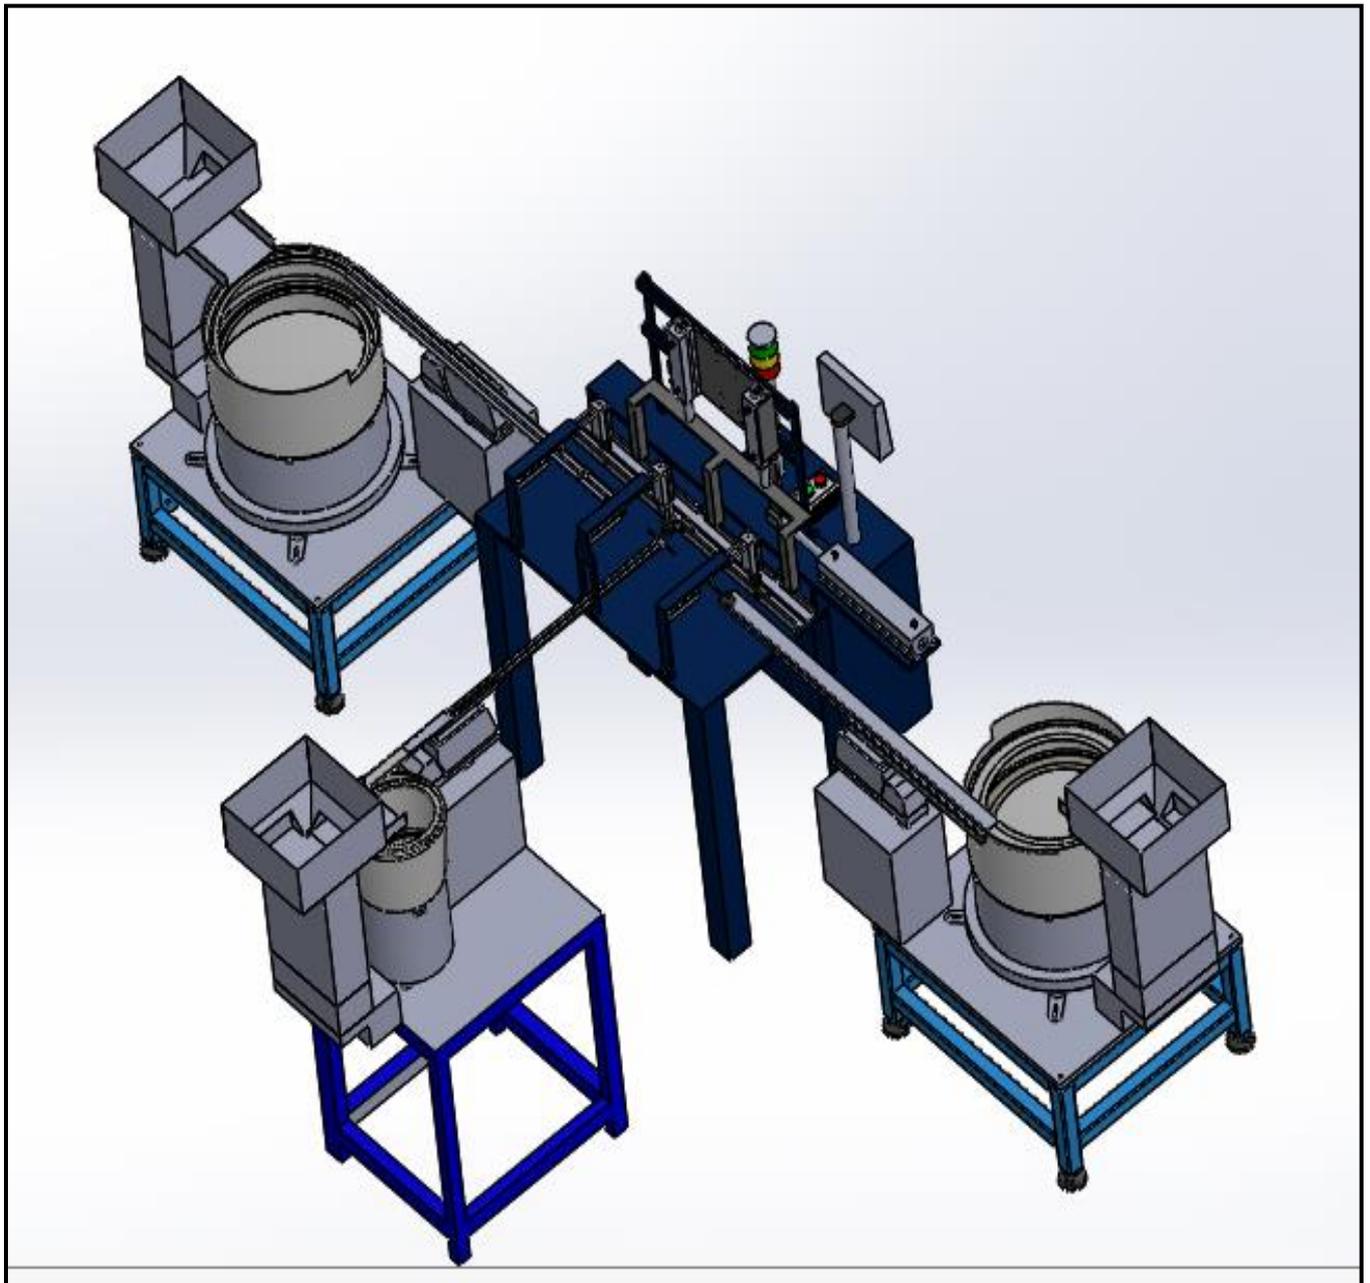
conception finale de la machine d'assemblages des pièces d'une prise électrique
